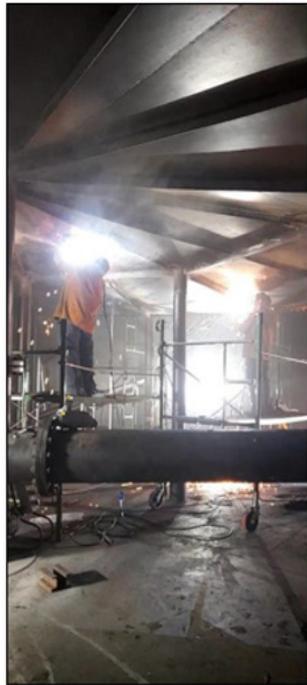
4-5 Soldadura en espacio confinado con andamio en tanque cortador, planta sur
